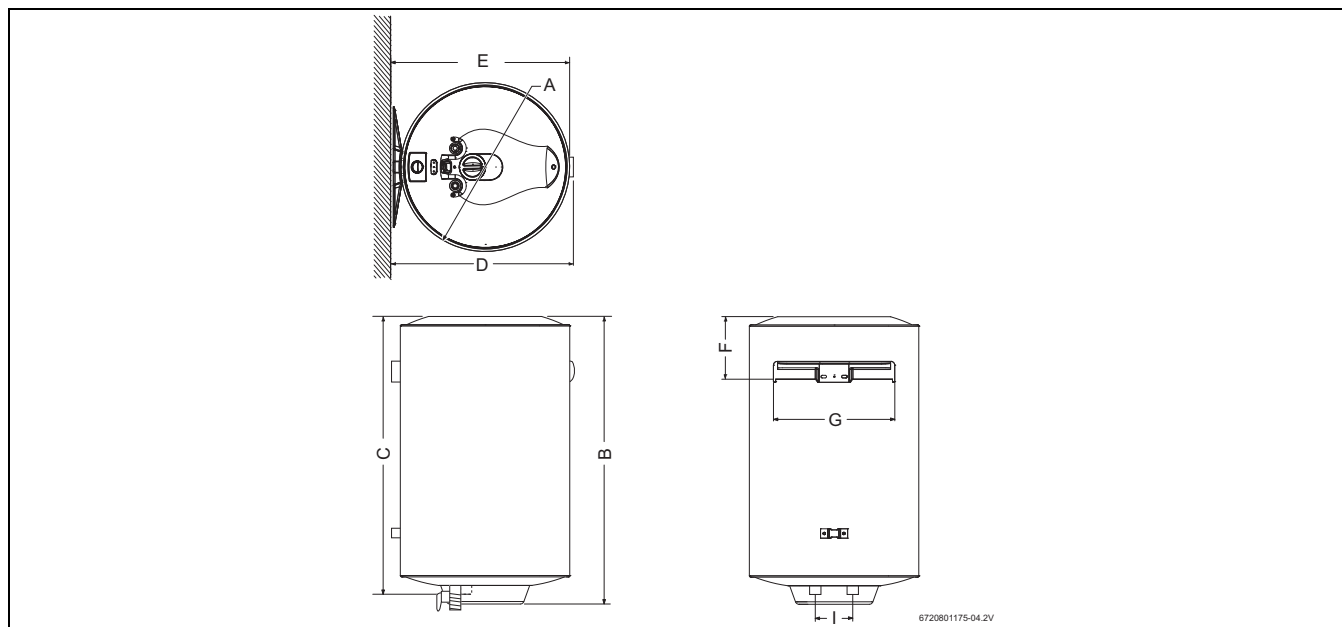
Dimensiuni în mm (ES035/050/080/100/120-4...)
